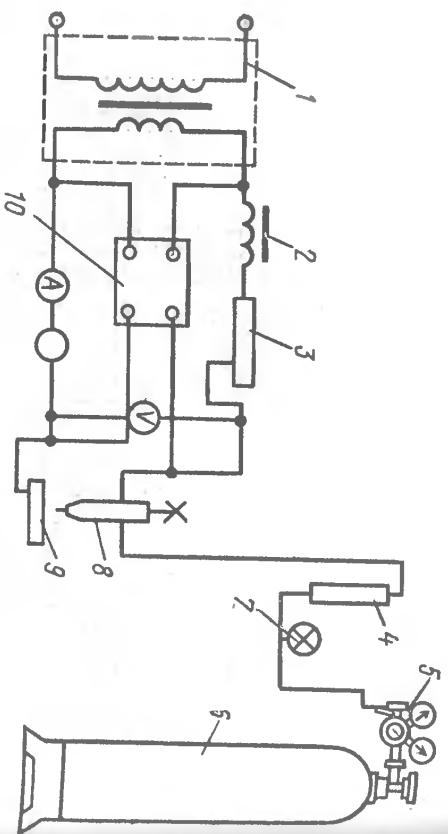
Схема сварки в инертных газах на переменном токе:
